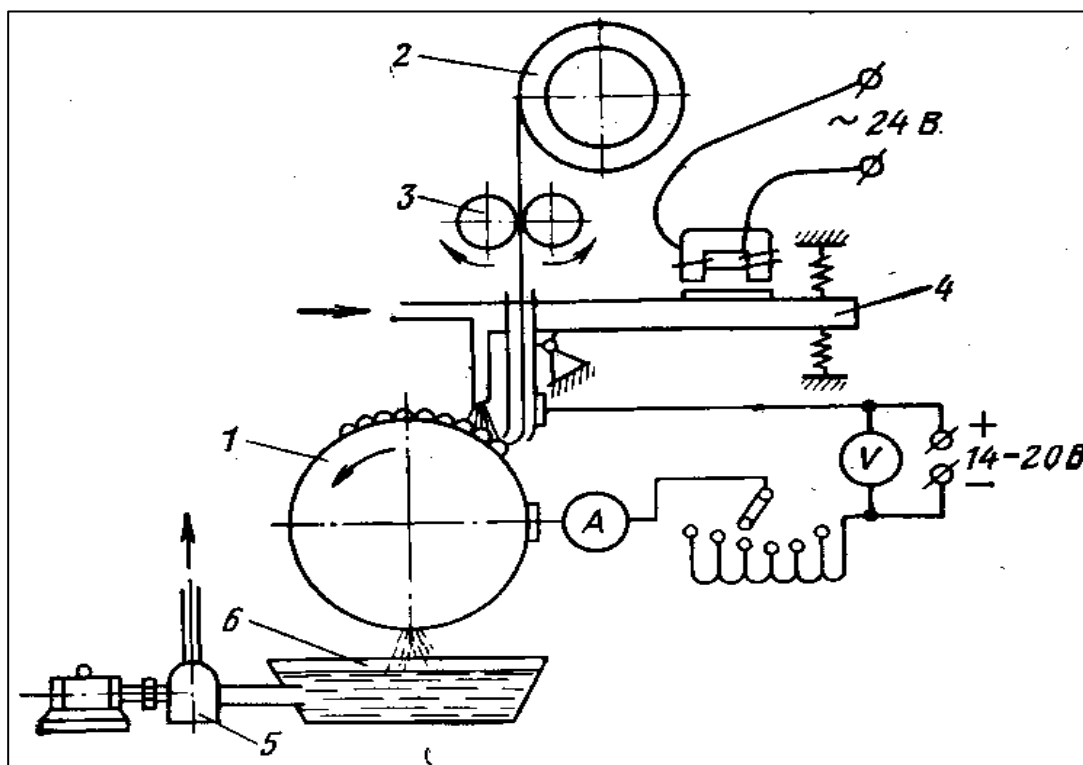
Схема установки для вибродуговой наплавки деталей:
